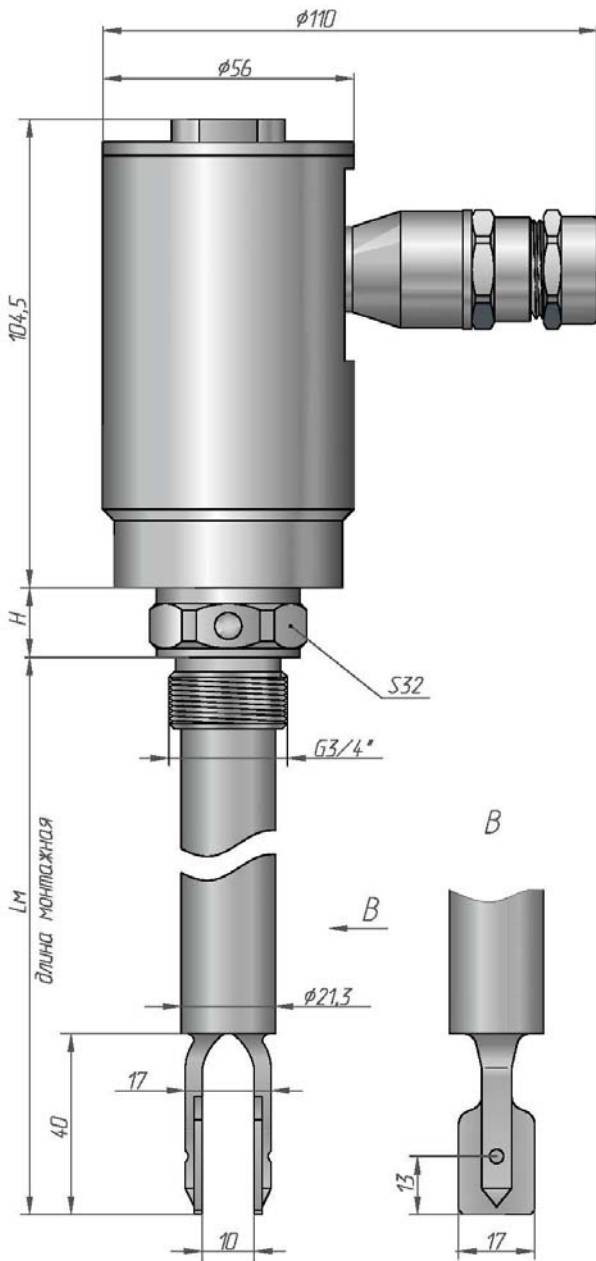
Габаритно-установочный чертеж ВИСУР
